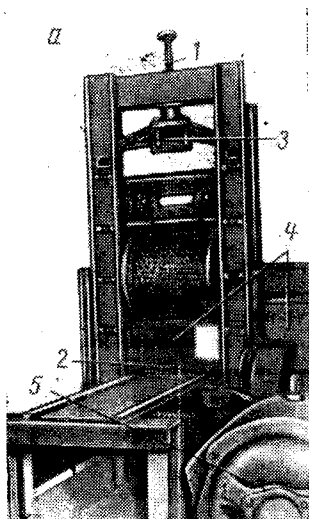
Опытный станок ЦНИИС для накальвания древесины:
